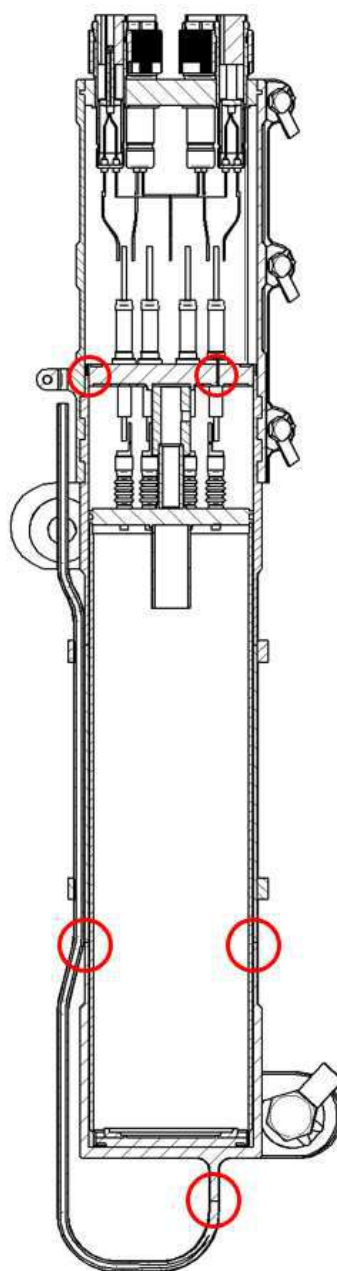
Конфигурация сварных соединений диверторного монитора нейтронного потока ИТЭР, подлежащих проверке после изготовления.
